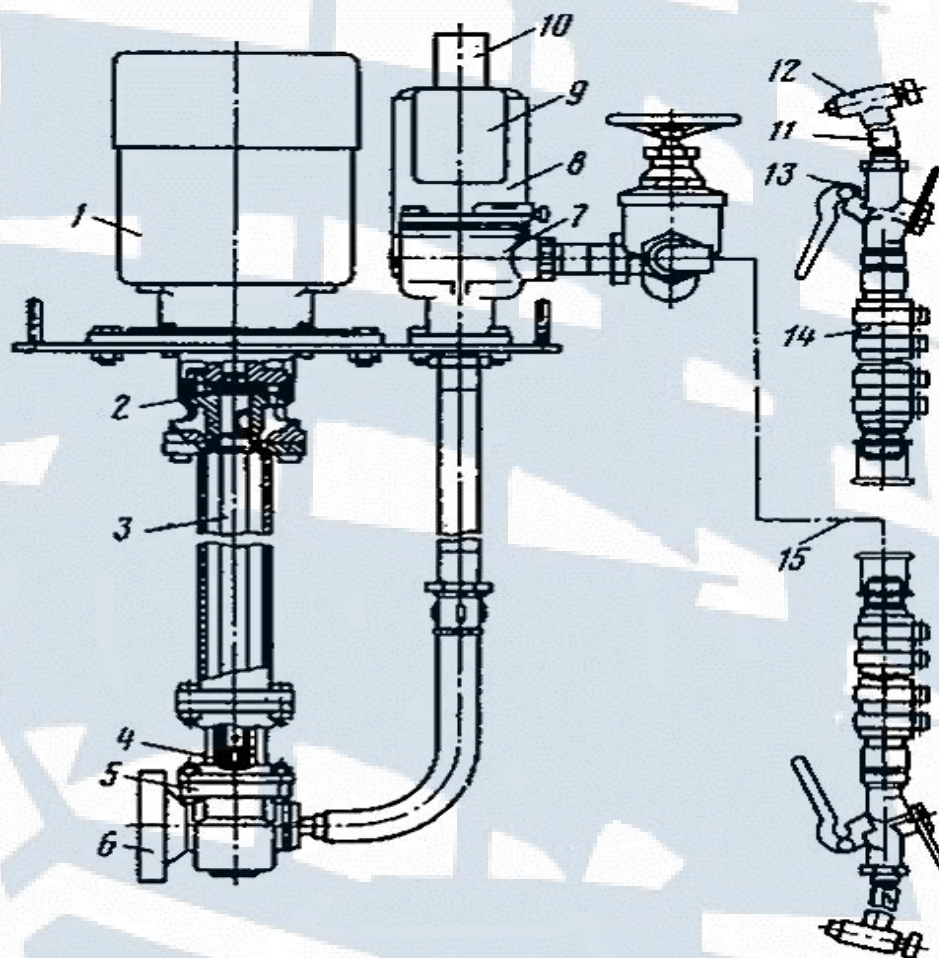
Схема установки для заправки трансмиссионными маслами агрегатов:
